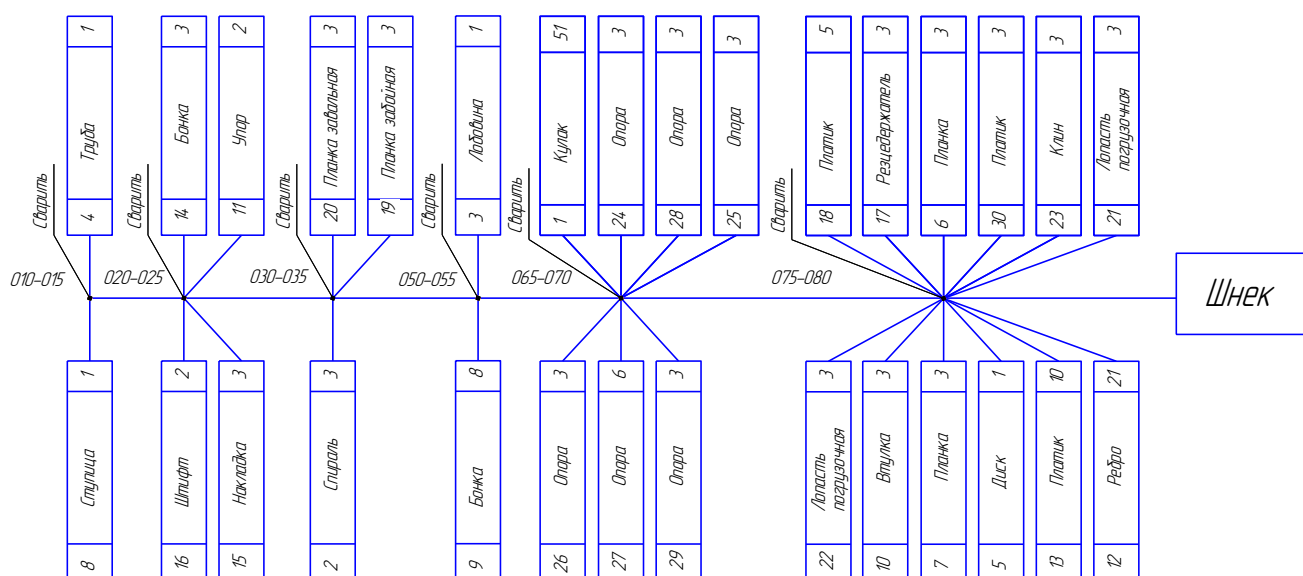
Технологическая схема изготовления шнека сварного
